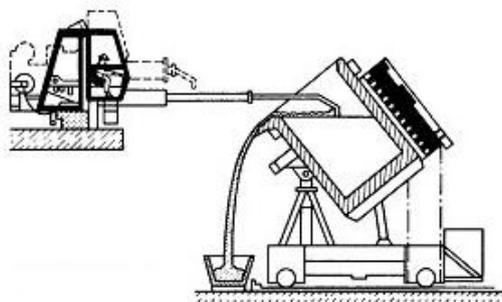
Установка для скачивания шлака с поверхности металла в ковше
